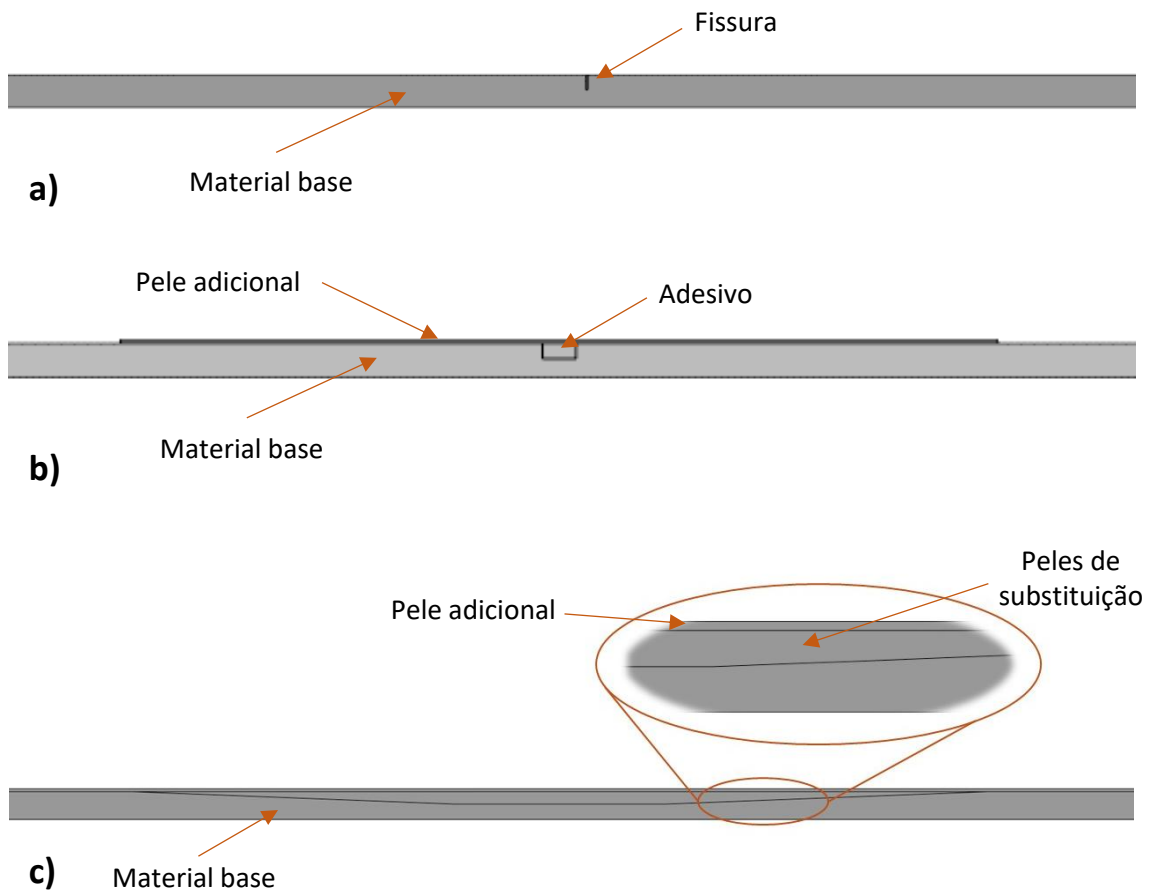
Geometrias da zona de reparação: a) fissura pré-reparação; b) reparação por preenchimento de adesivo; c) reparação por substituição das peles danificadas, em formato de escalonado
